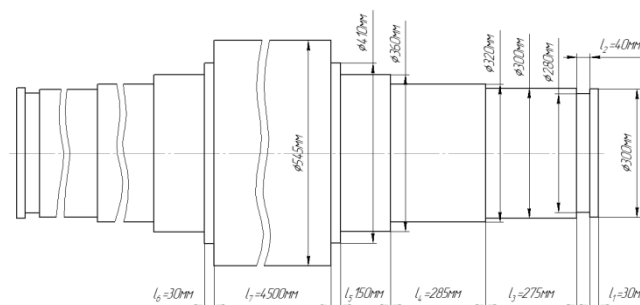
Розрахункова схема цапф приводного вала
